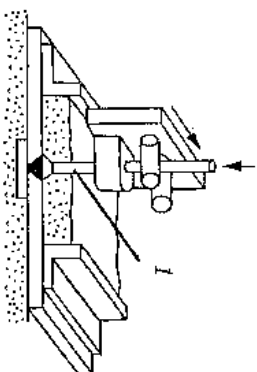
Автоматическая дуговая сварка под слоем флюса
